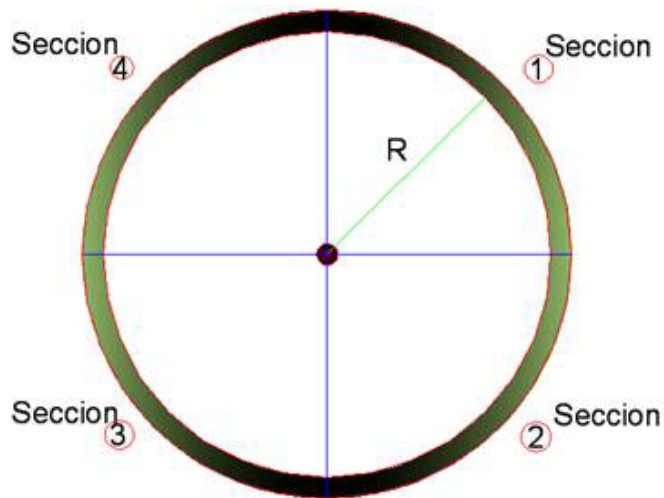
Seccionamiento de tuberías 16 mm a 90 mm
